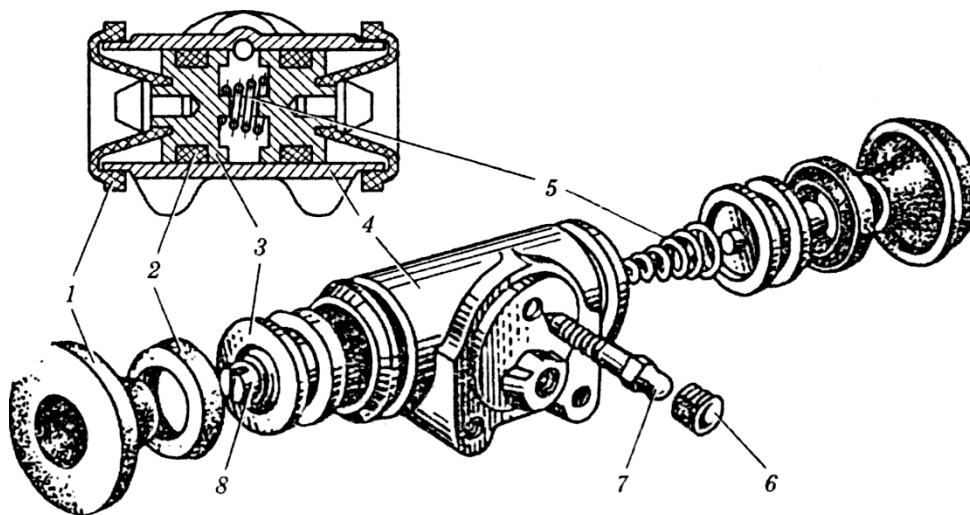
Колісний поршневий гідроциліндр гальм:
